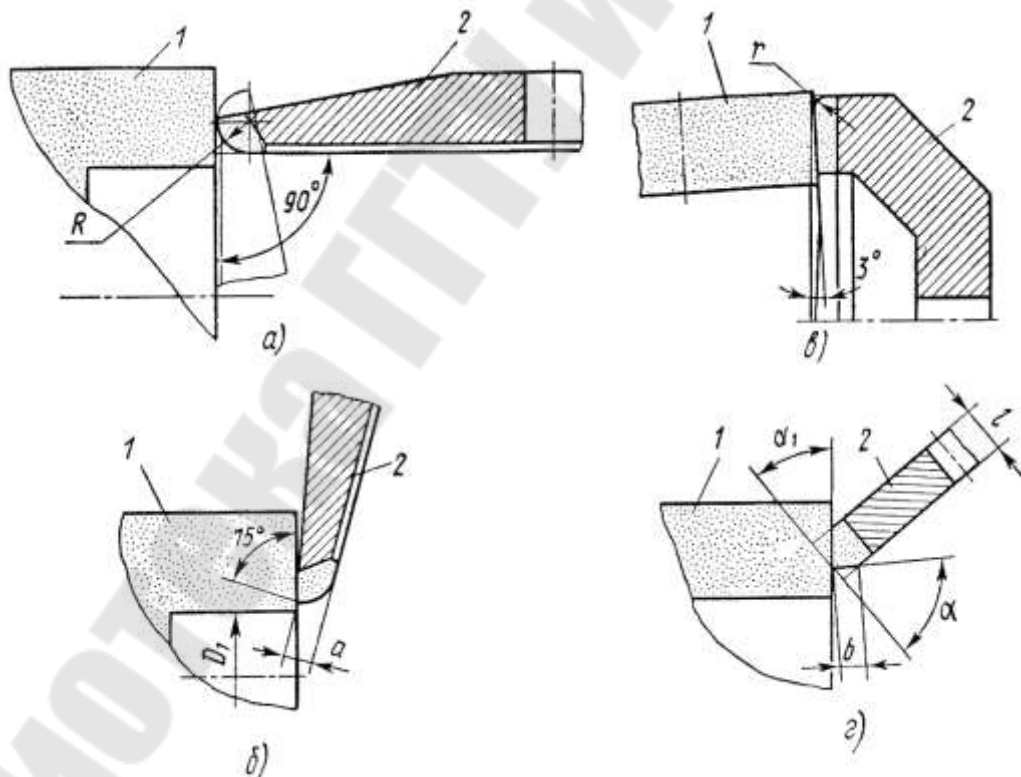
Схемы правки методом шлифования алмазных и эльборовых инструментов при вышлифовке канавок сверл (*a, б*); метчиков и разверток с прямыми зубьями (*в*); фрез и разверток с винтовыми зубьями (*г*): 1 – правящие абразивные инструменты; 2 – алмазные инструменты
